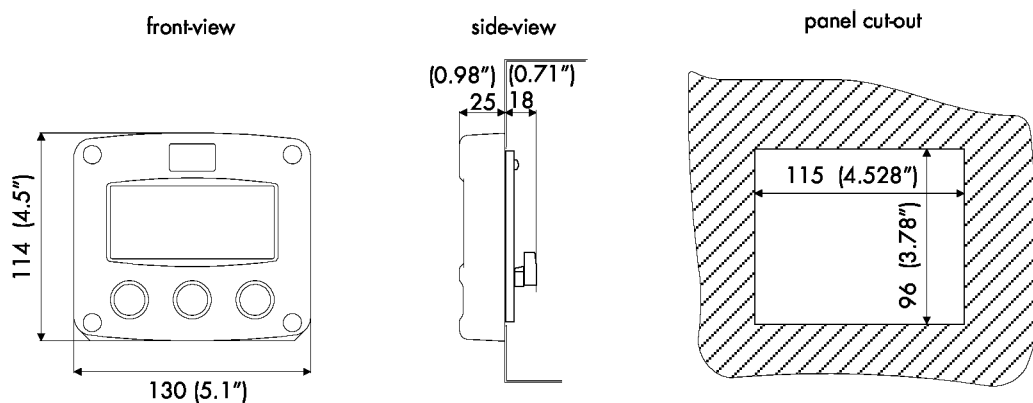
Abmessungen für Standard IP65/NEMA 4 Aluminium Gehäuse und Ausschnitt. (MTL662)
